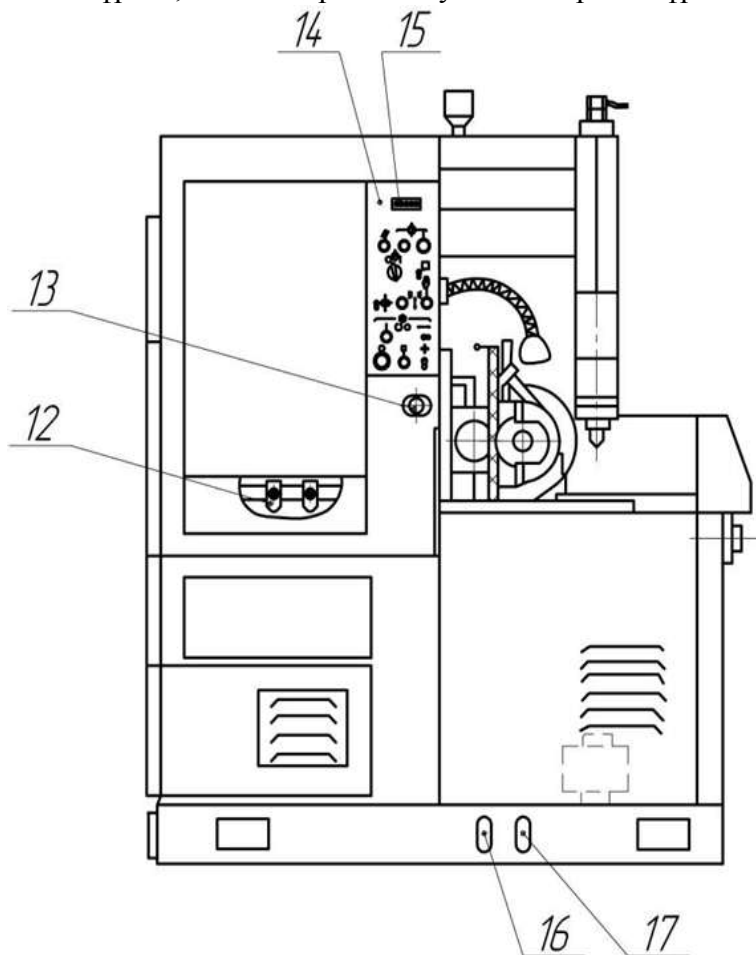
Органи керування верстатом 5B312, вигляд ліворуч: 12 – упори встановлення переміщення фрезерного стояка; 13 – квадрат повертання супорта; 14 – пульт керування під час налагодження;
